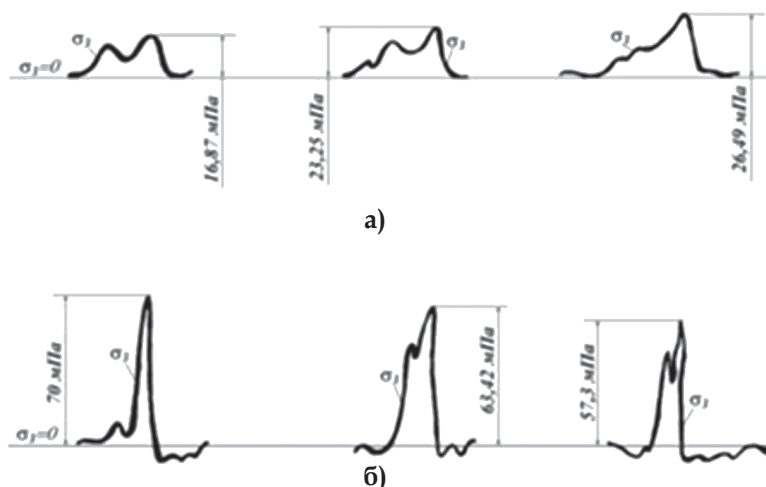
Изгибные напряжения в зубе шестерни открытой зубчатой передачи мельницы МРГ 5500x7500:
